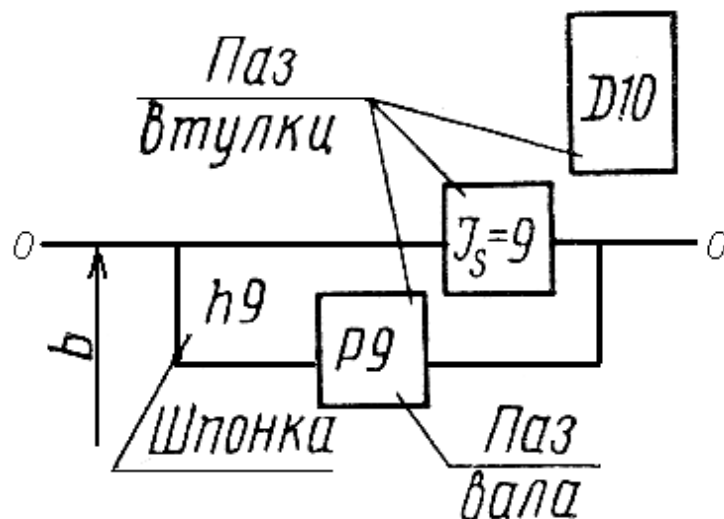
Поля допусків для ширини призматичної шпонки, паза вала і втулки
